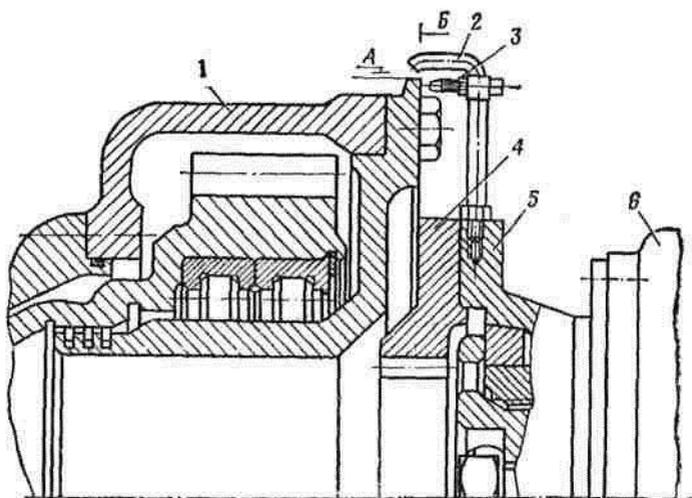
Установка приспособления 172.91.055С6 для центровки двигателя с гитарой танка Т-72:
